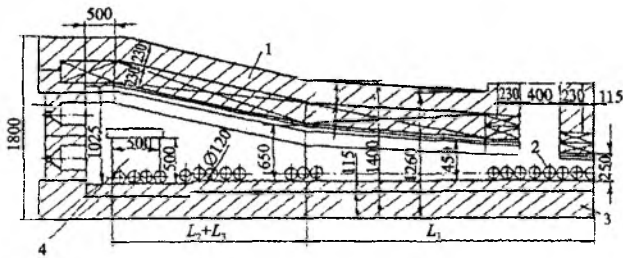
(к примеру 6.2). К расчету рабочего пространства методической нагревательной печи с торцевой загрузкой и боковой выдачей заготовок: 1 — свод рабочего пространства; 2 — нагреваемая заготовка; 3 — под рабочего пространства; 4 — окно выдачи нагретых заготовок
